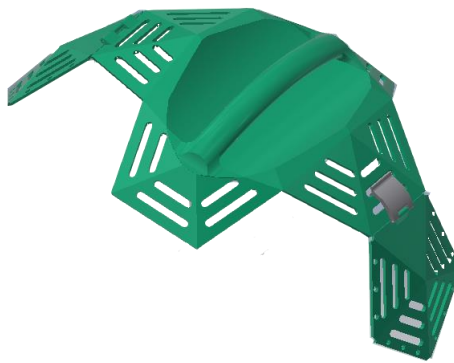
35 Ensamblaje de la tapa del tambor.
